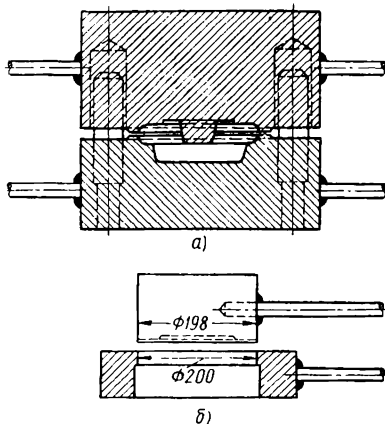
Изготовление поковки чашки: а — подкладной штамп; б — подкладной «обрезной инструмент»
